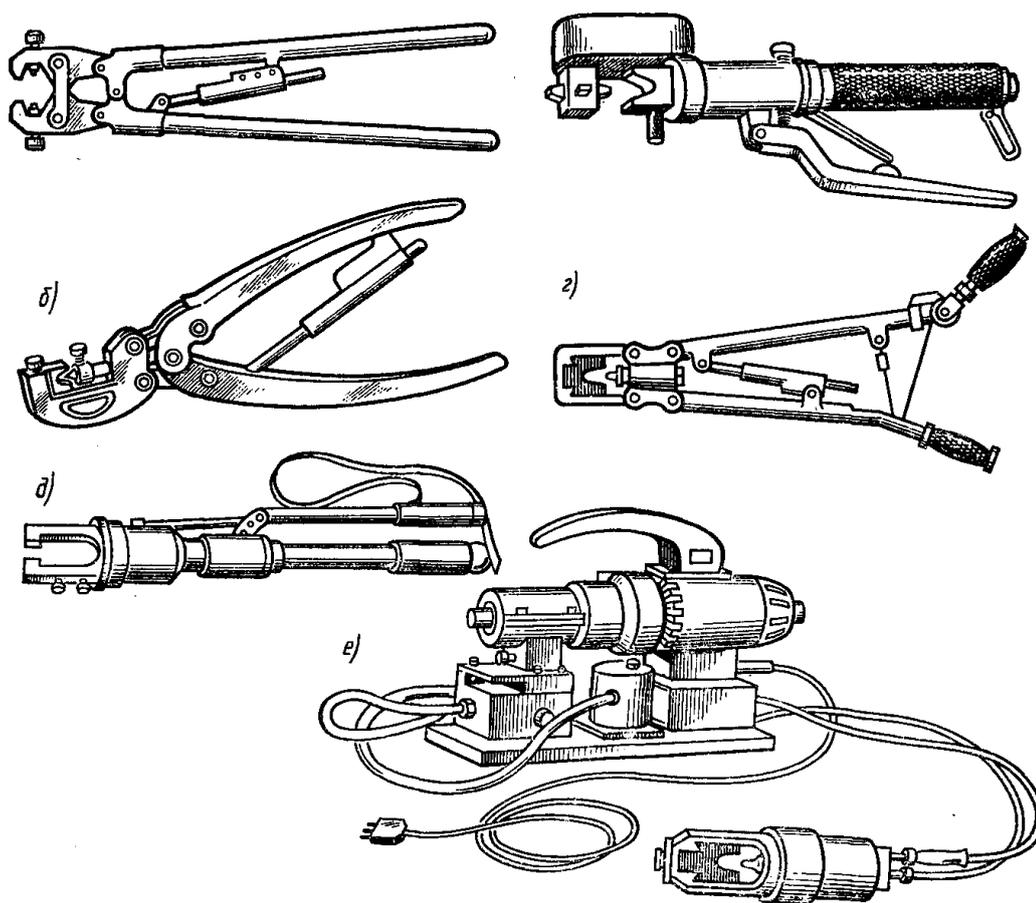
Инструменты и механизм для опрессовки наконечников и гильз:
